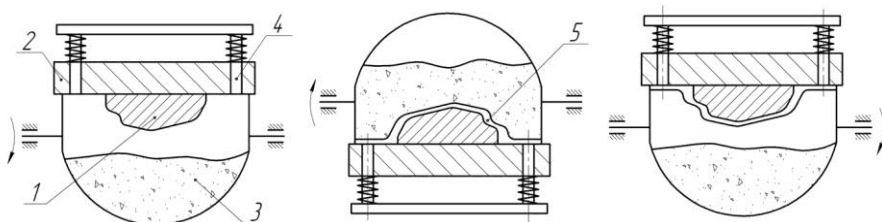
Схема виготовлення оболонкової форми:
